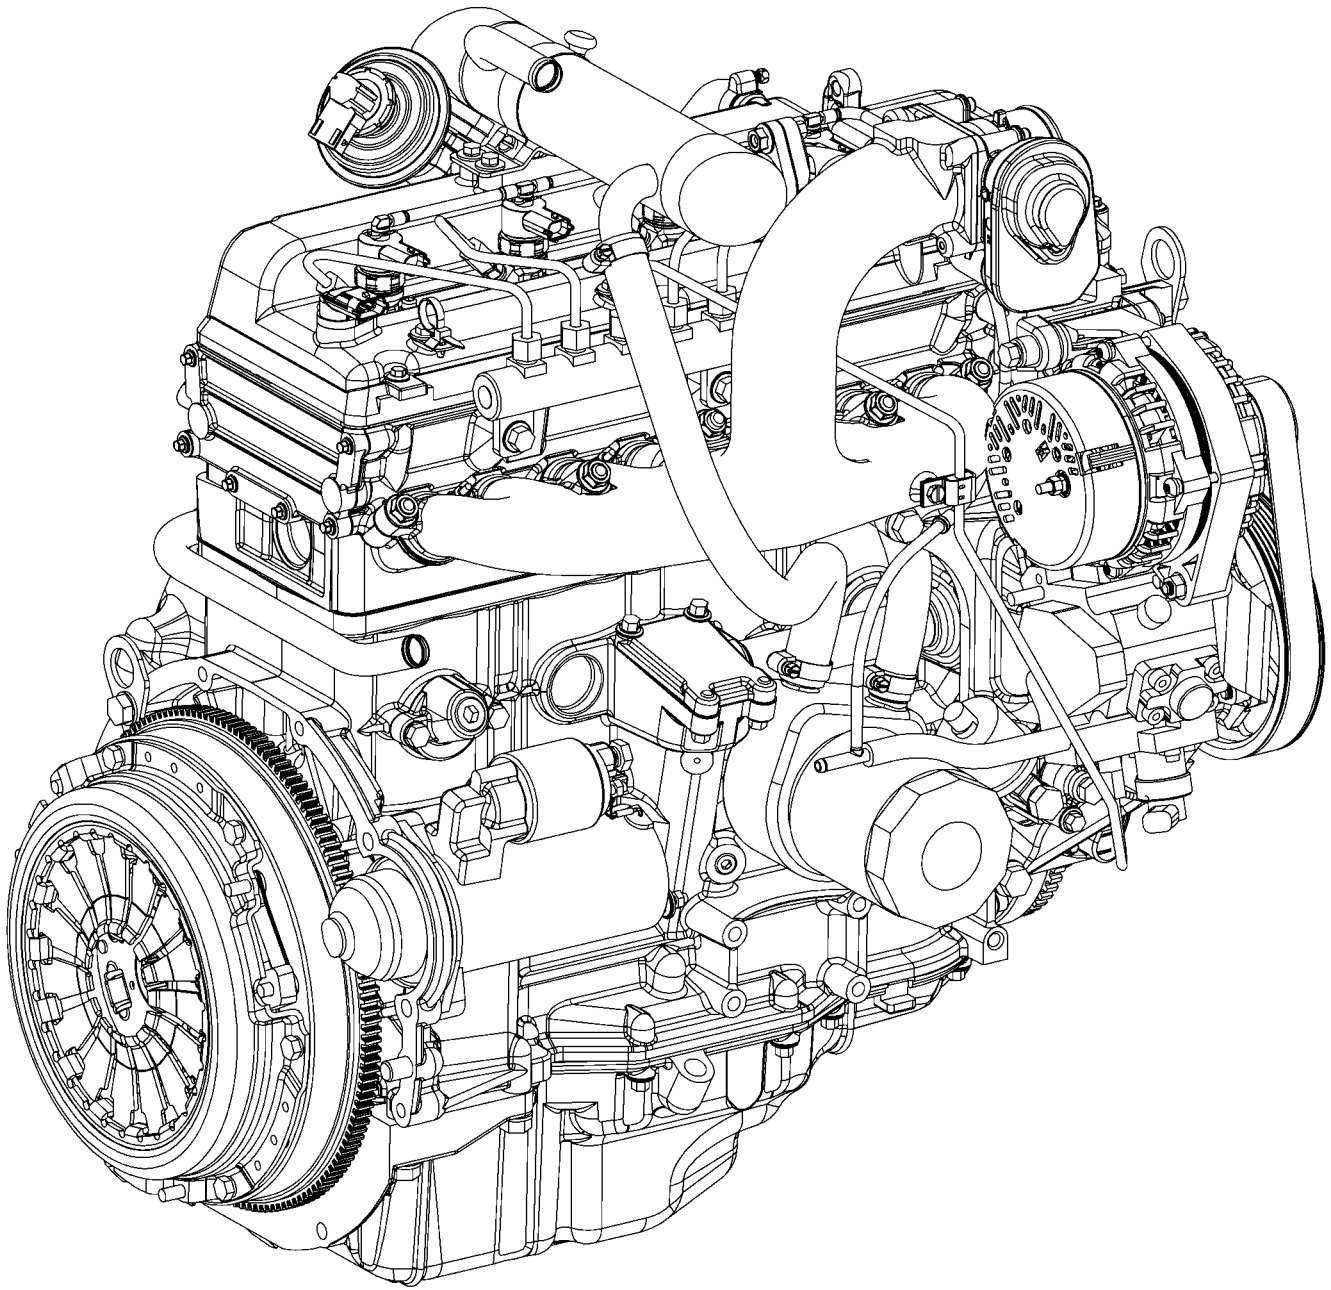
в. Внешний вид двигателя без компрессора кондиционера, насоса ГУР и деталей привода вентилятора
